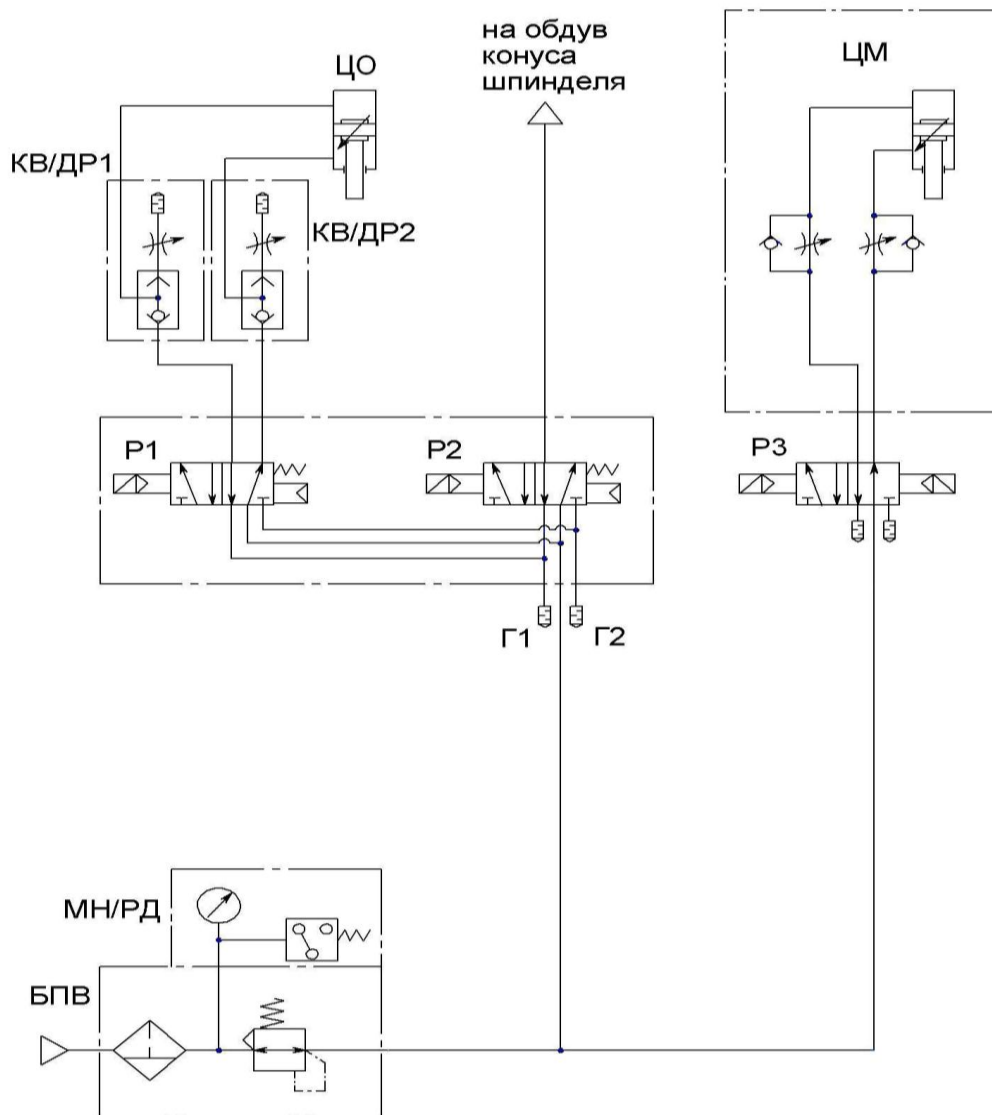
Пневморазводка по станку с манипуляторным инструментальным магазином
